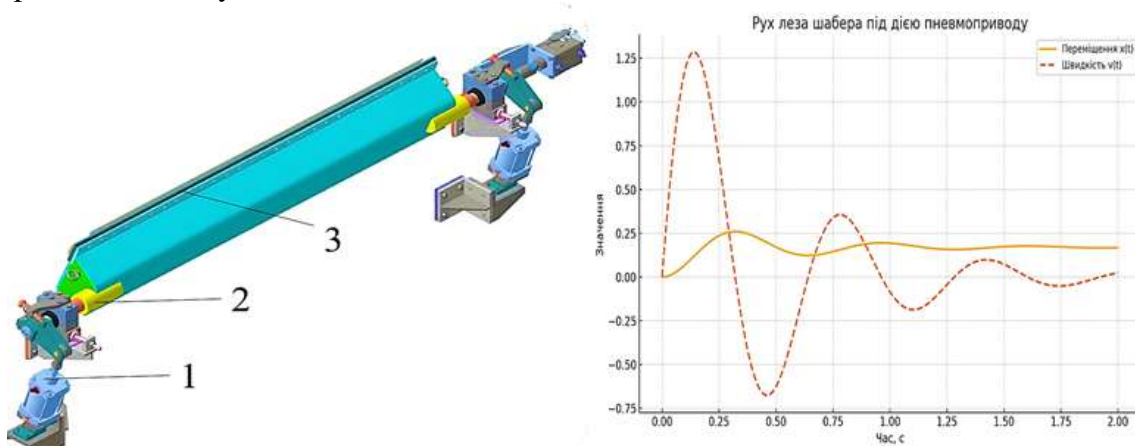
Загальний вид та кінематичні характеристики шабера пресового валу з механізмом осциляції: 1- привід, 2- корпус, 3 - лезо
